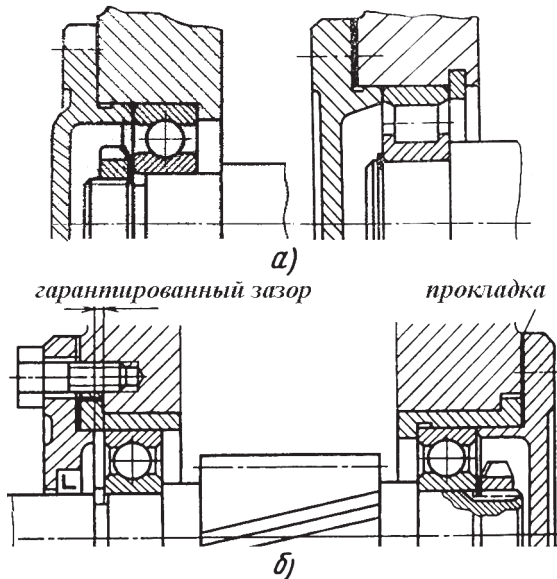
Конструкция узла опоры с фиксированным подшипником, выполненной непосредственно в корпусе (а) и в стакане с плавающей опорой (б)
